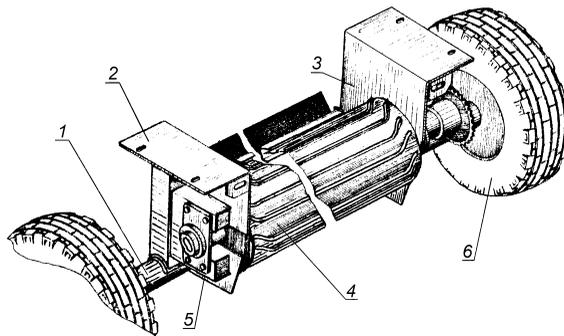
Основание камеры: 1 – ось; 2 и 3 – боковины; 4 – валец нижний задний; 5 – корпус подшипника; 6 – колесо
